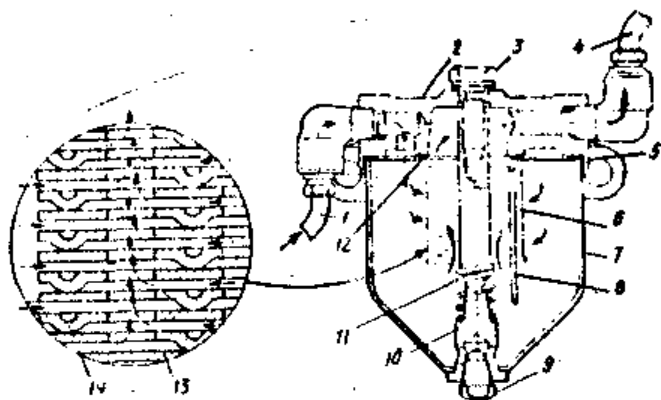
Фільтр-відстійник: 1, 4 – введення і виведення палива; 2 – корпус; 3 – стяжний болт; 5, 12 – прокладки; 6 – фільтрувальні елементи; 7 – стакан; 8 – встановлювальні стержні; 9 – пробка зливного отвору; 10 – стяжний стержень; 11 – пружини; 13 – пакет тонких латунних дисків; 14 – дистанційні виступи на дисках
